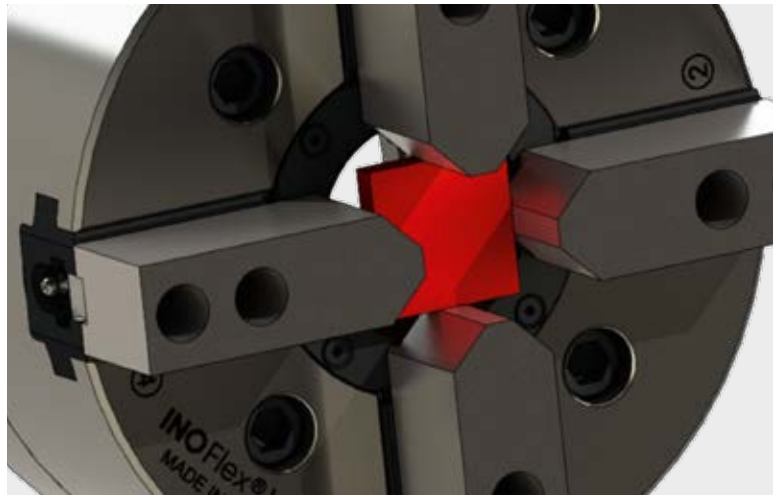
gespannter Ausdrehkern / Fig. 2 Clamped masterpiece
